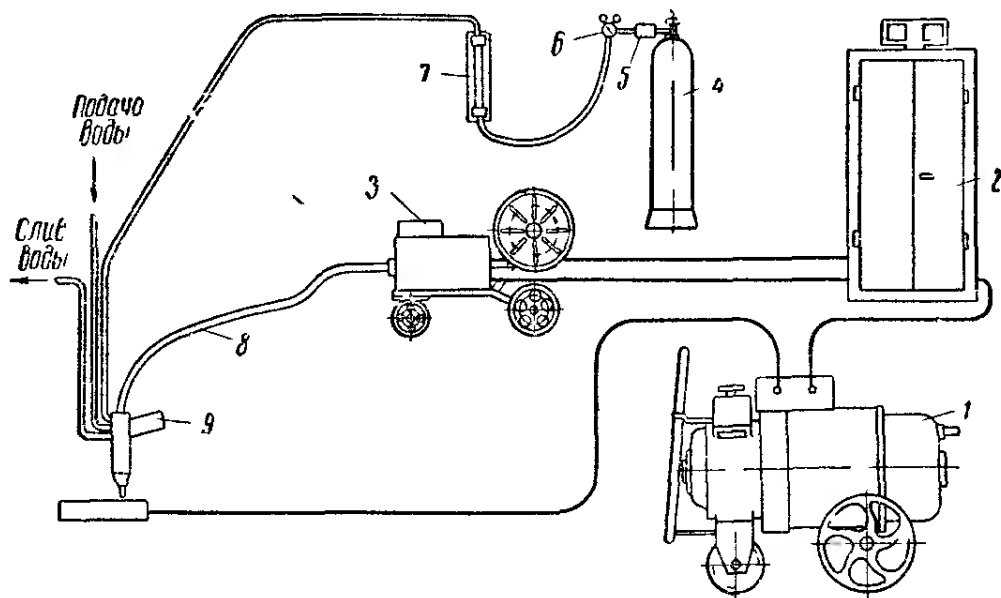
Схема установки для полуавтоматической сварки плавящимся электродом в среде углекислого газа:
